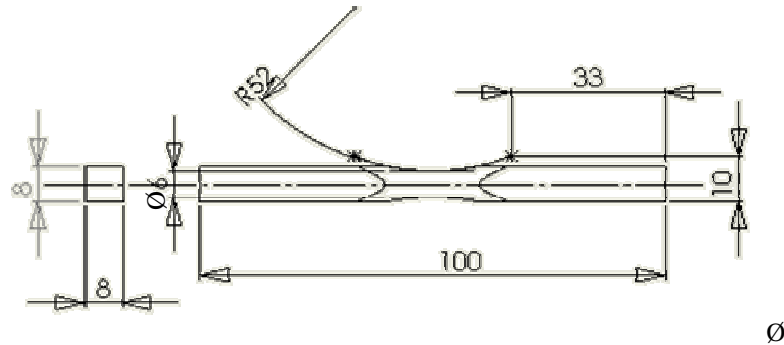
Géométrie d'éprouvettes utilisées pour les essais de fatigue sous chargement de torsion (AlSi7Cu05Mg03)
